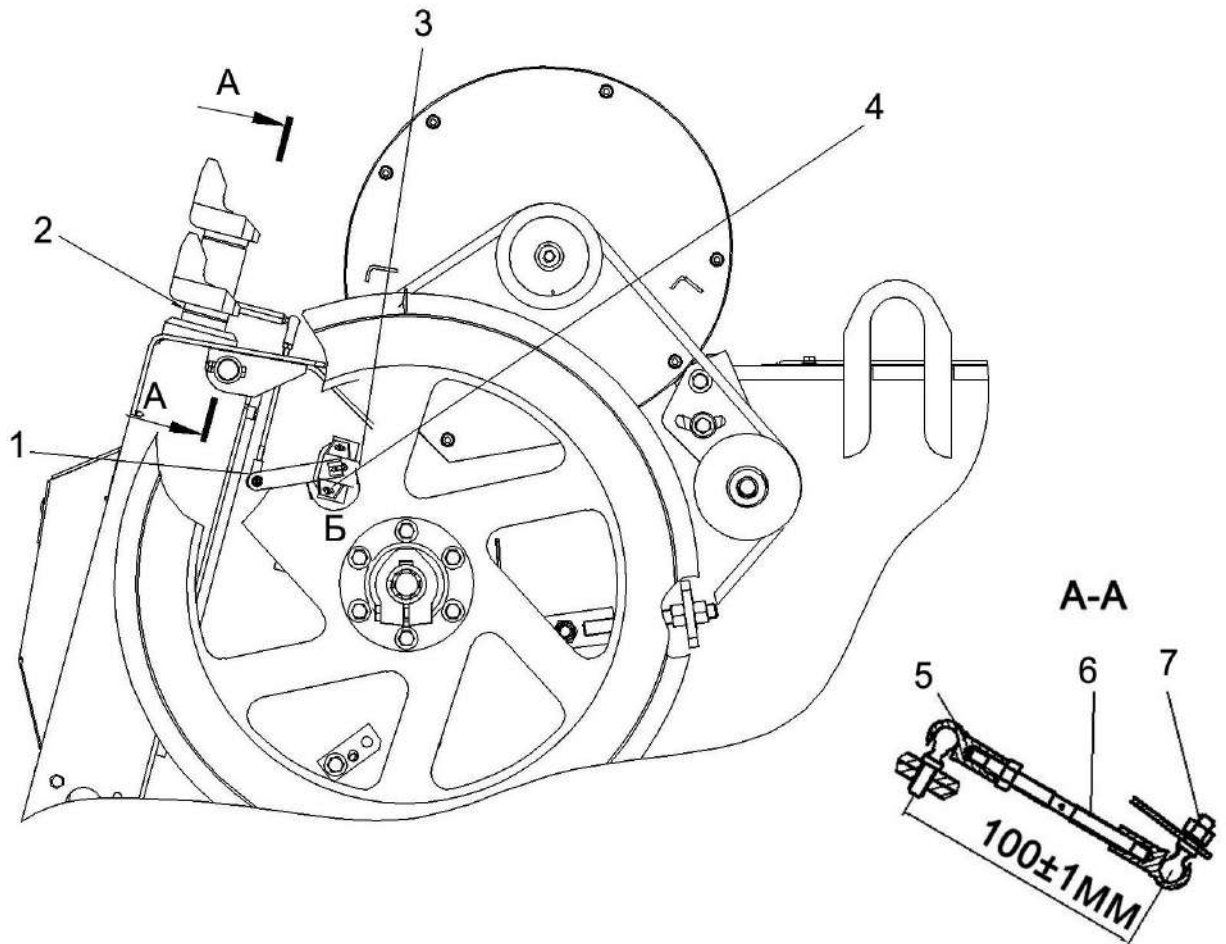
Регулировка цепной передачи привода мотовила
